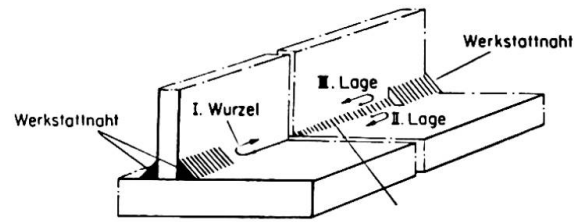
Einzelheit zu Fig. 8. CO₂-Schweißfolge der Montage-Halsnaht.
